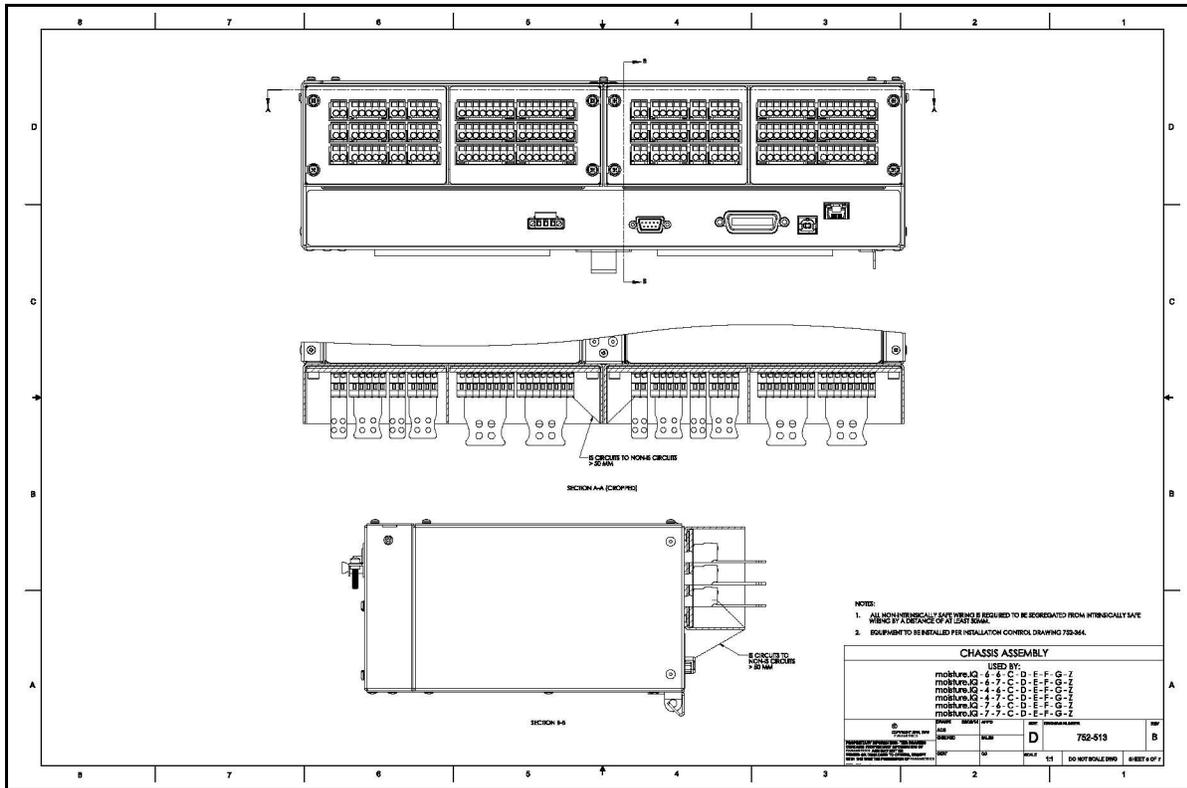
Gehäuse-Baugruppe (Zeichnung 752-513_revB, Blatt 5 von 5)
